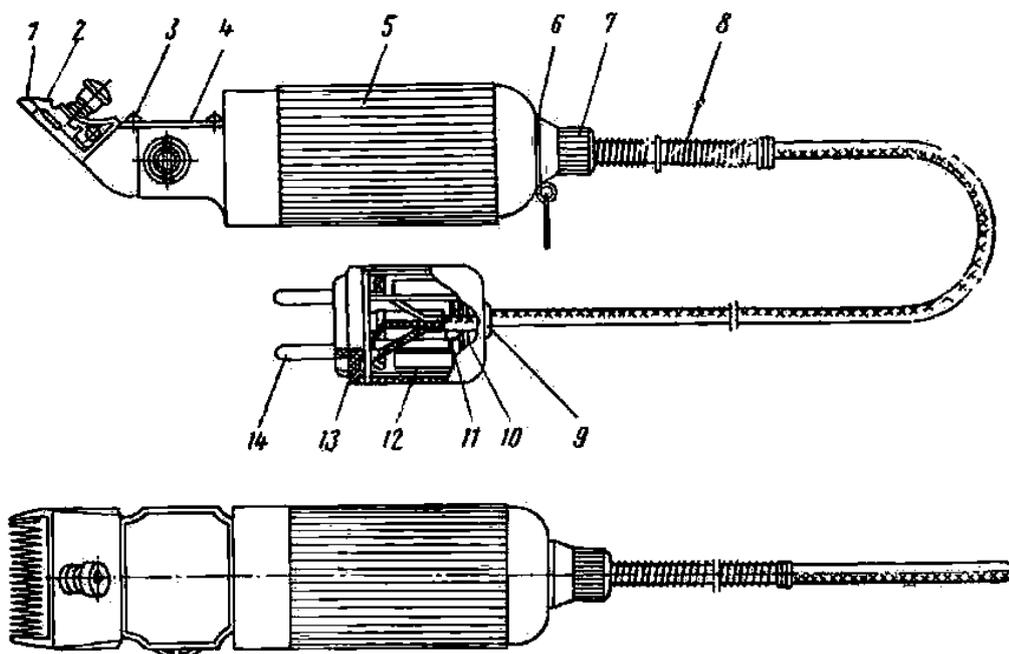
Электрическая машинка для стрижки волос: 1 и 2 - ножи; 3- винт; 4-крышка головки ножевого блока; 5 - кожух машинки; 6 - ушко; 7 - гайка; 8 - пружина; 9 - корпус вилки; 10 - планка; 11 и 13 - винты; 12— картон электроизоляционный; 14 - штифт вилки
